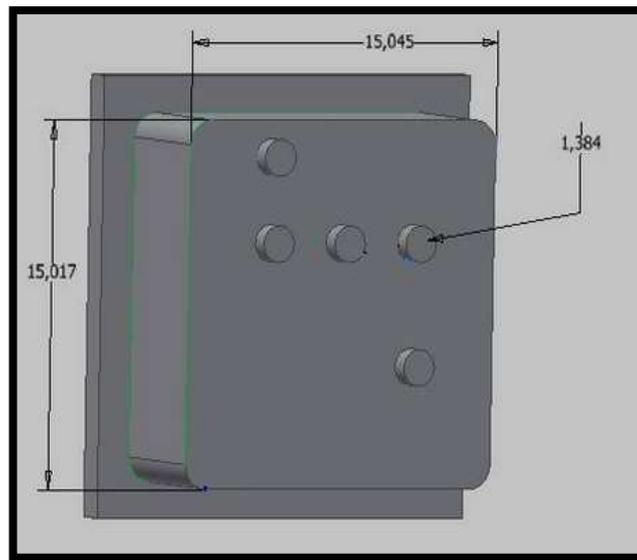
Dimensiones de cada tecla del Sistema Embebido
